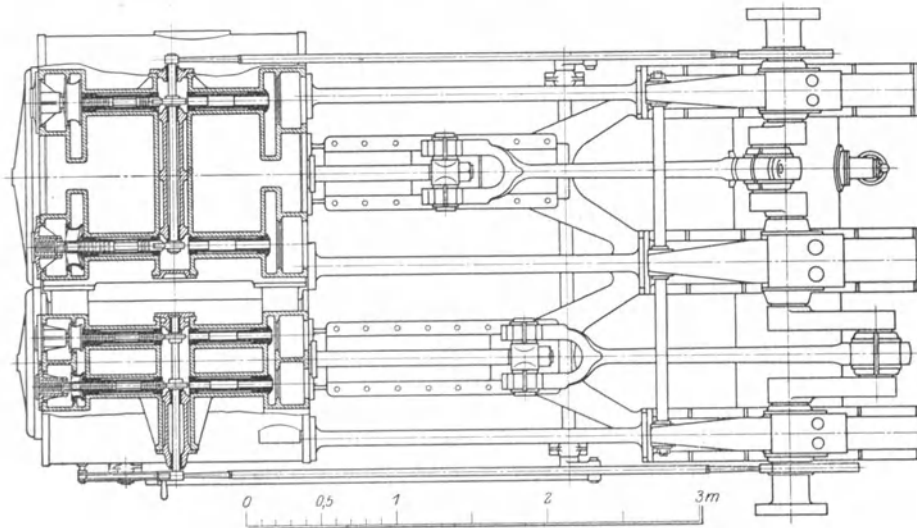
Radschiffsmaschine mit Lentz-Ventilen (Aufsicht).
